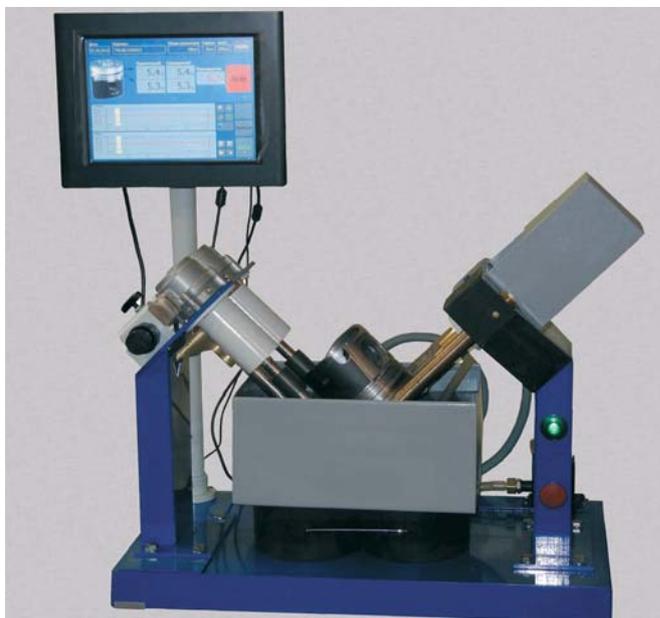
Установка для неразрушающего контроля качества сцепления нирезистовых вставок в поршнях дизельных двигателей
